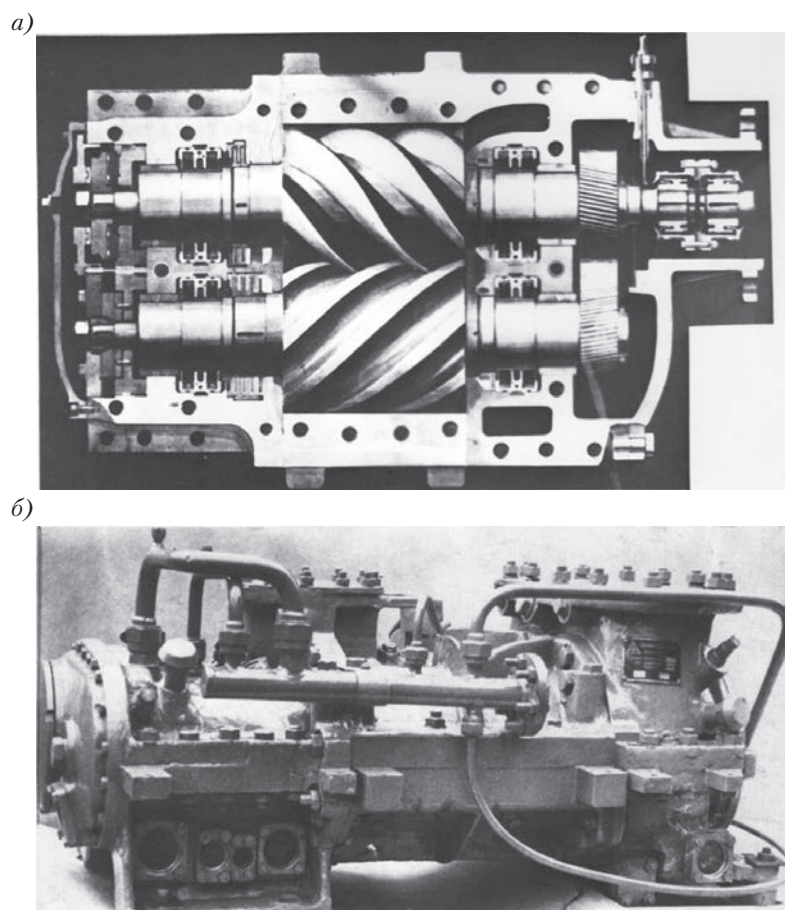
Компрессор марки ВК (а) и марки ВК5 (б)
